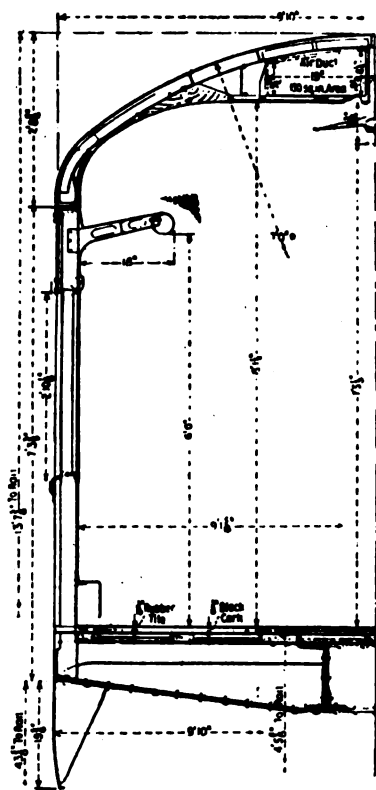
Illuminazione semi-indiretta: doppia canarola contenente lampade, situata alla mezzzeria del soffitto, e lampade a illuminazione diretta, fissate al bordo delle reti porta-bagagli.
